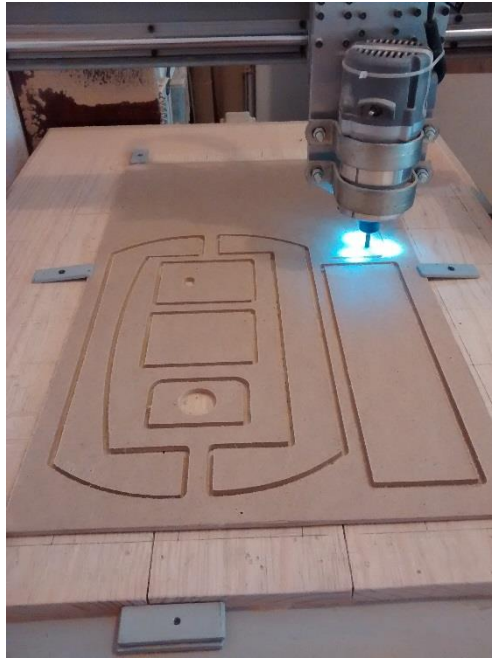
Maquinado con la estrategia perfilado de las piezas del puente de la impresora.
